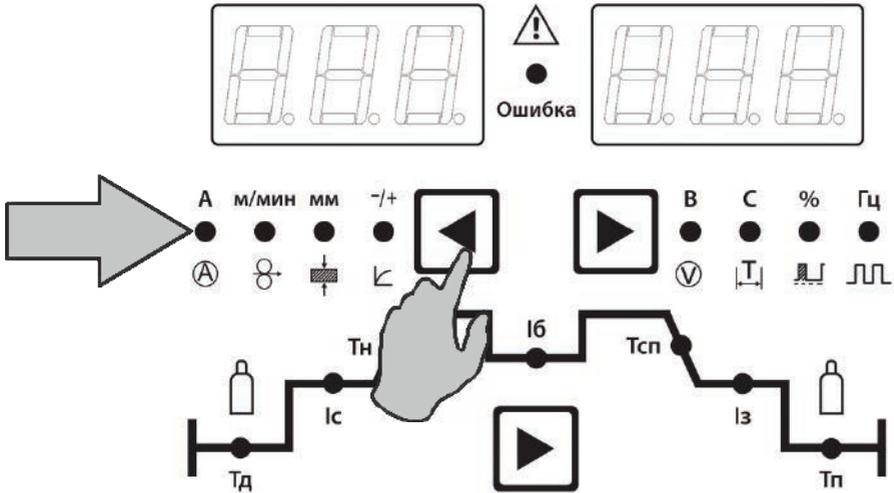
Установка пикового сварочного тока и напряжения на дуге.
